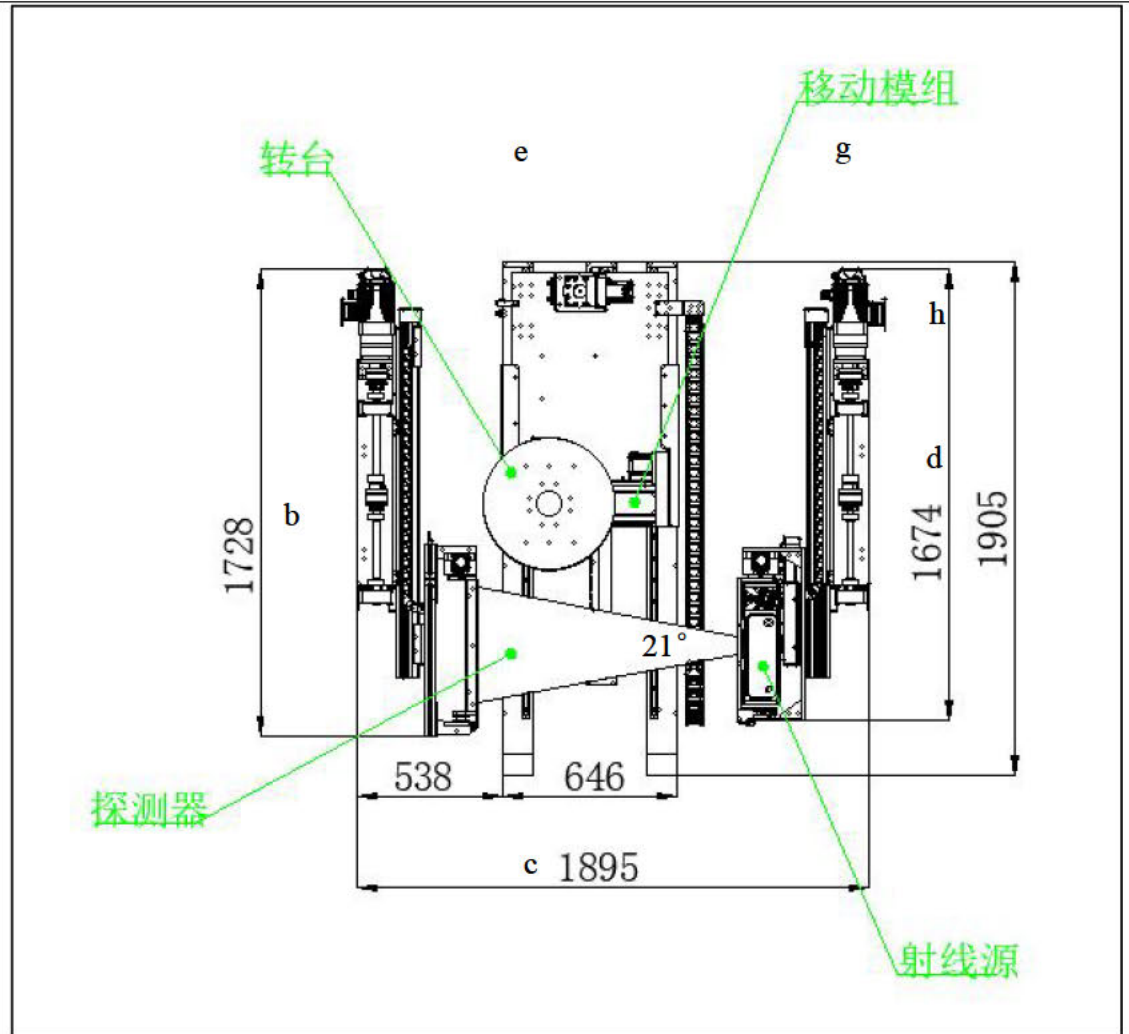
本项目铅房内部组件平面布局示意图（单位：mm）
